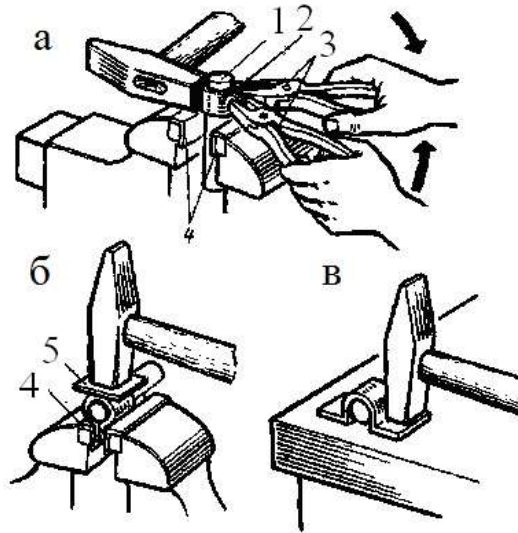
Прийоми виготовлення згинанням хомутика: 1 – оправка; 2 – заготовка; 3 – плоскогубці; 4 – нагубники; 5 – мідна пластина.
